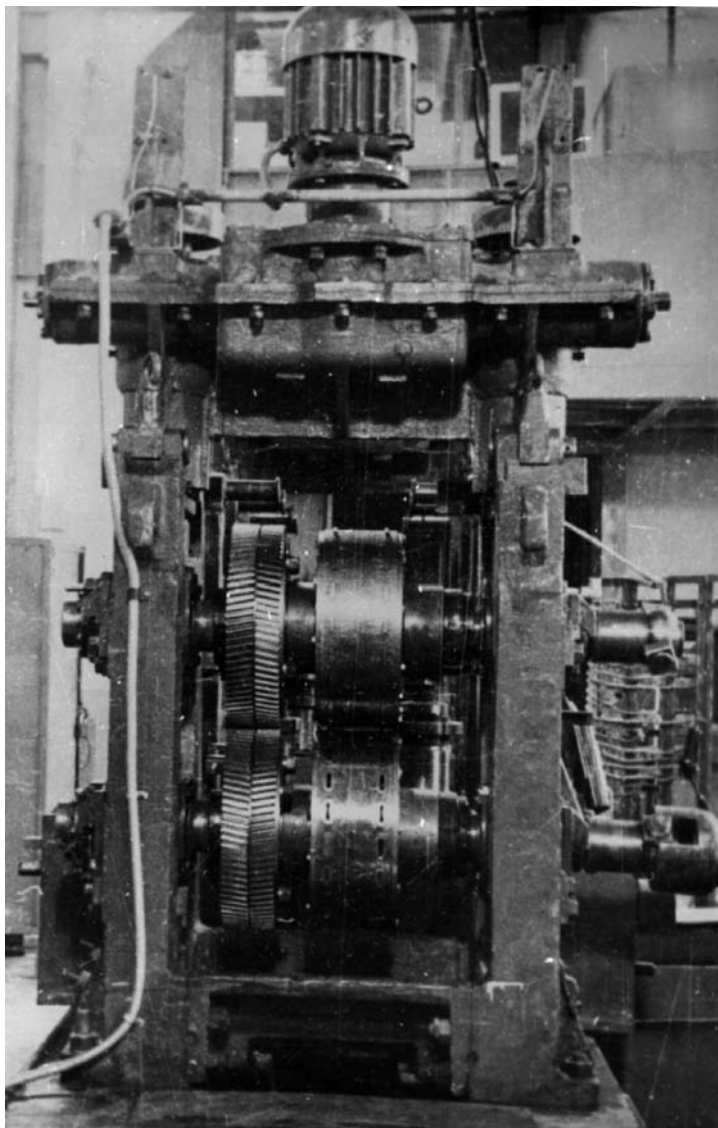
Рабочая клетка механизма валковой перфорации
